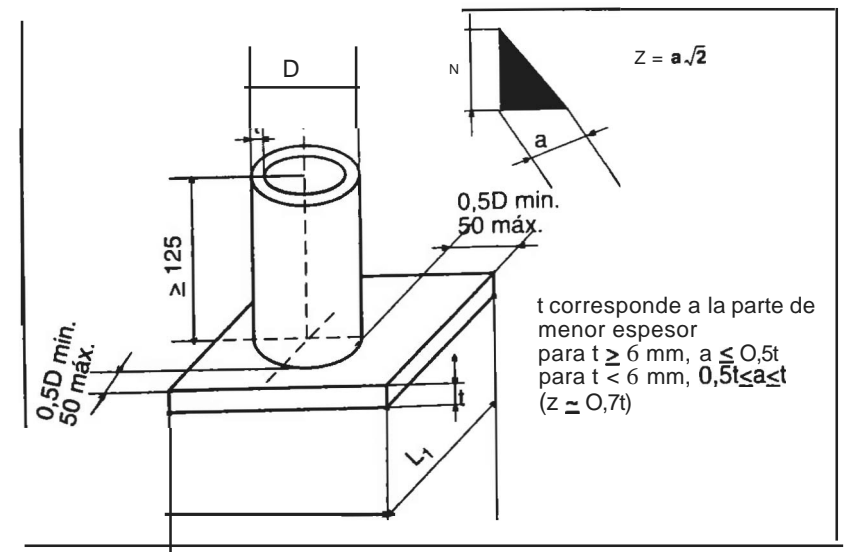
DIMENSIONES DEL CUPÓN DE PRUEBA PARA EL SOLDEO DE TUBOS EN ÁNGULO (DIMENSIONES EN MILÍMETROS)
